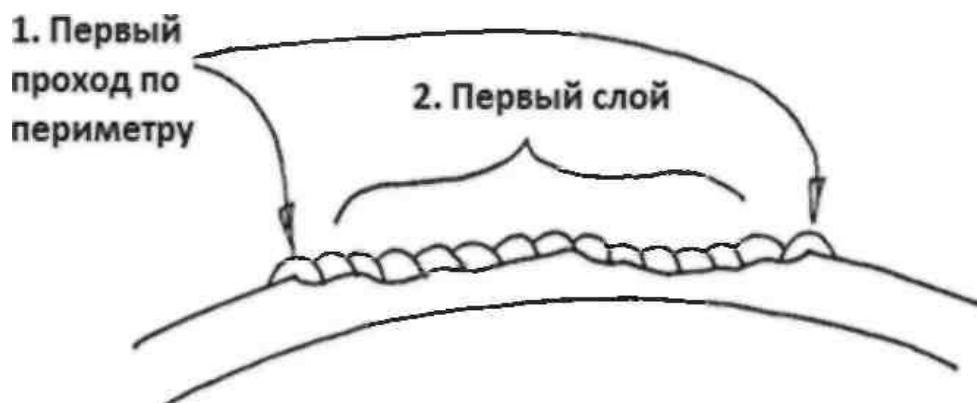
Схема наложения первого слоя сварочной наплавки
